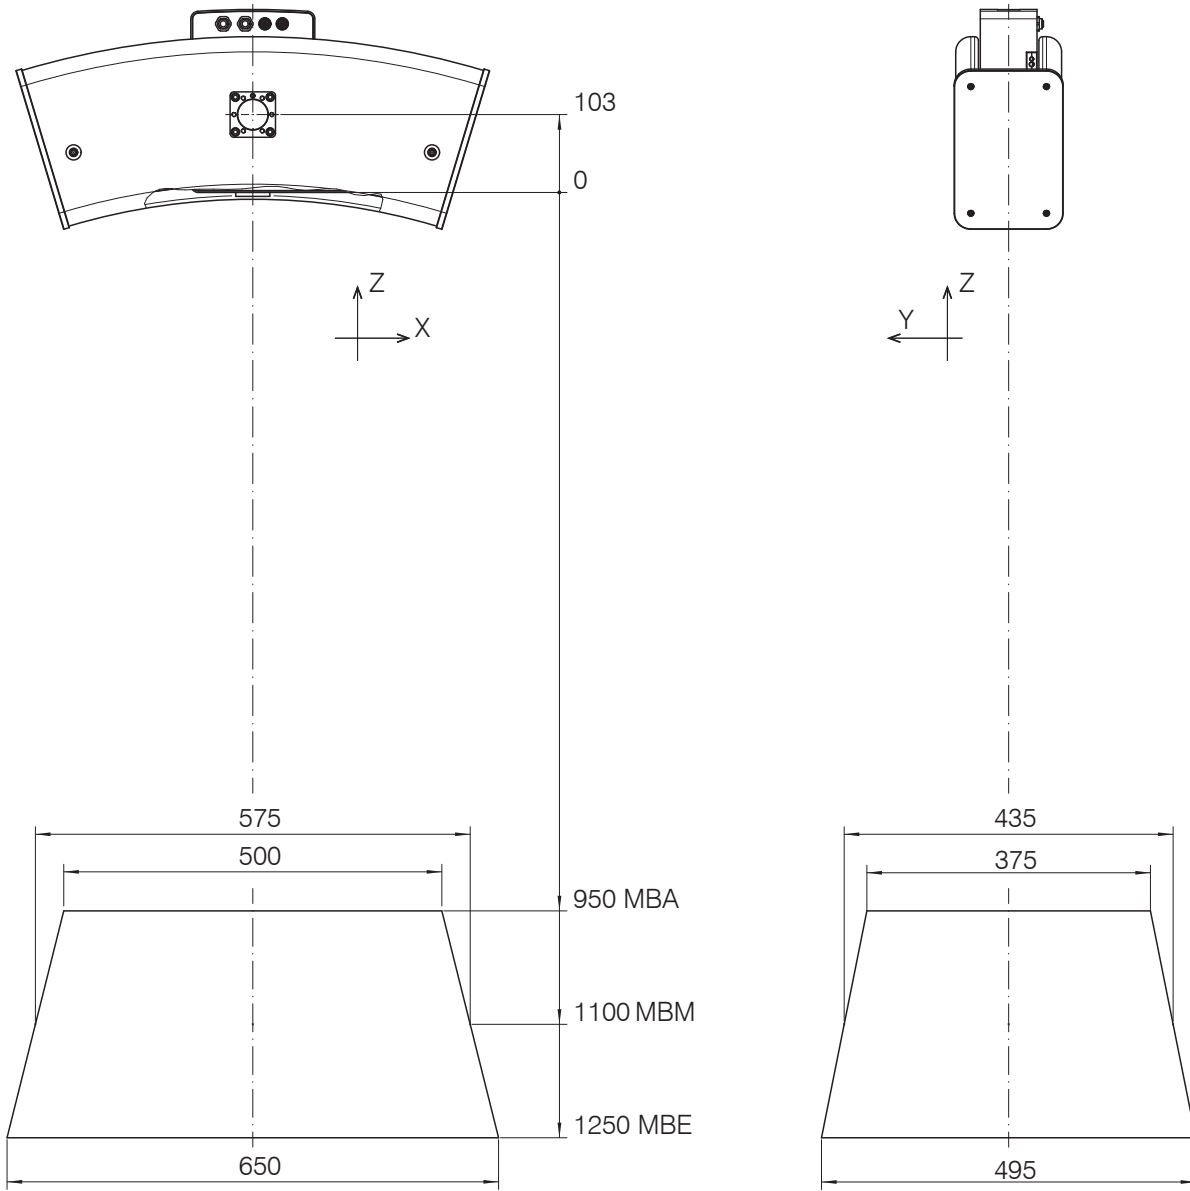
Maßzeichnung Messfeld surfaceCONTROL 3D SC25x0-575
